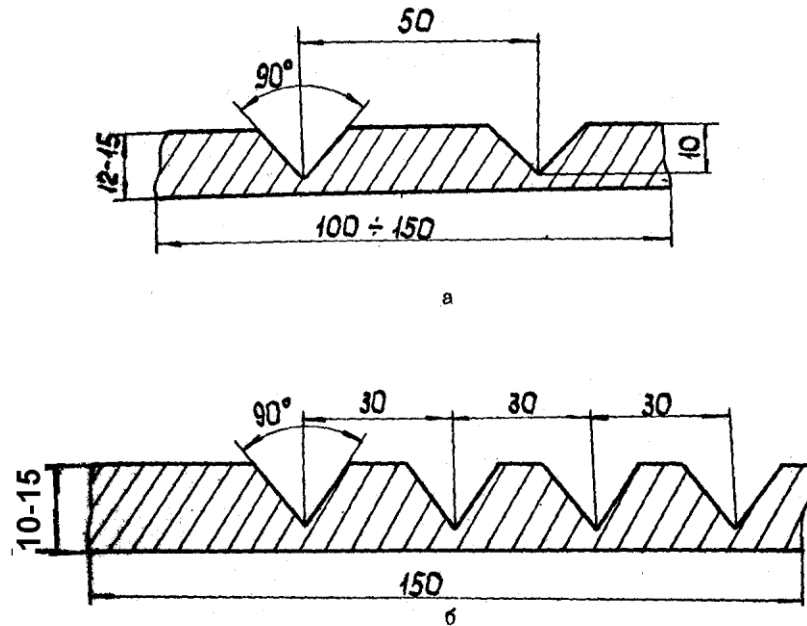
Схема підготовки крайок для зварювання чавуна:
